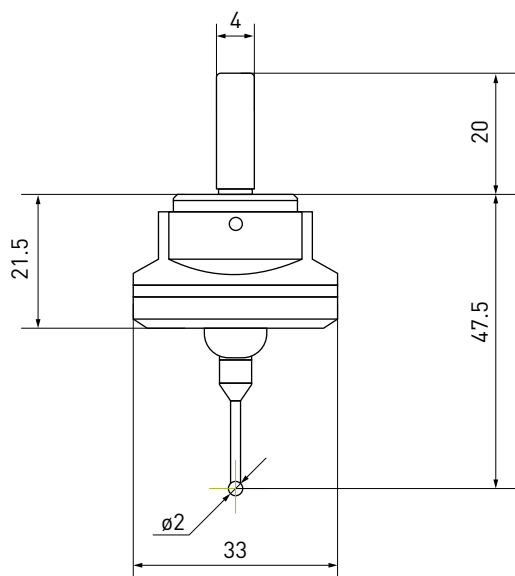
Габаритный чертеж измерительного датчика PL-V4.
